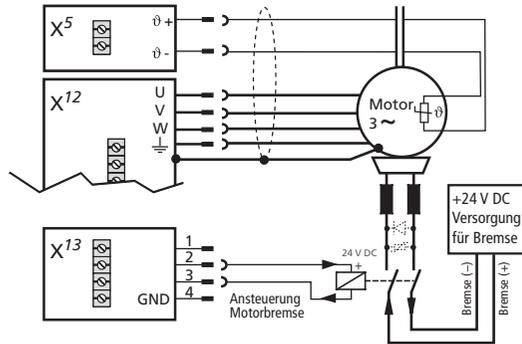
Anschluss des Motors bei BG1 bis BG4 (Motorbremse ab 2 A)
